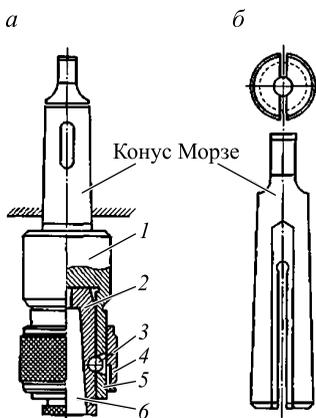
Быстросменный сверлильный патрон (а) и коническая втулка для крепления сверл с цилиндрическим хвостовиком (б): 1 — корпус патрона; 2 — сменная втулка; 3 — шарики; 4 — муфта; 5 — кольцо; 6 — оправка
